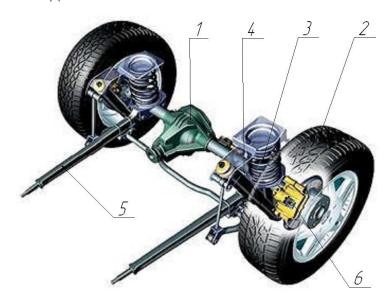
Зависимая подвеска: 1 — редуктор заднего моста; 2 — колесо; 3 — пружина; 4 — аммортизатор; 5 — реактивная штанга; 6 — ступица
